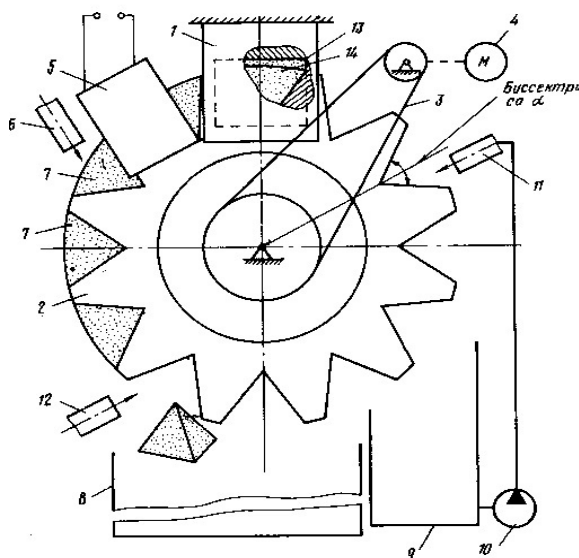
Схема работы устройства для прессования абразивных гранул преимущественно в форме тетраэдра [4]: 1 – фильера; 2 – приводной нож; 3 – клиноременная передача; 4 – электродвигатель; 5 – индуктор ТВЧ; 6 – форсунка; 7 – гранулы; 8 – бункер; 9 – бак с смазывающим материалом; 10 – насос; 11, 12- форсунки; 13 – основная полость; 14 – дополнительная коническая полость
